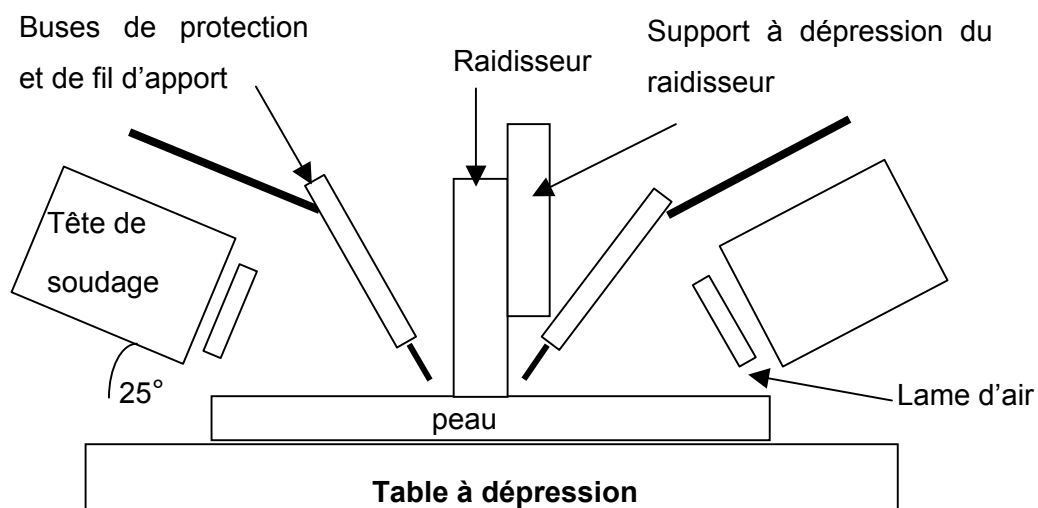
Schéma en coupe du dispositif de soudage en T
